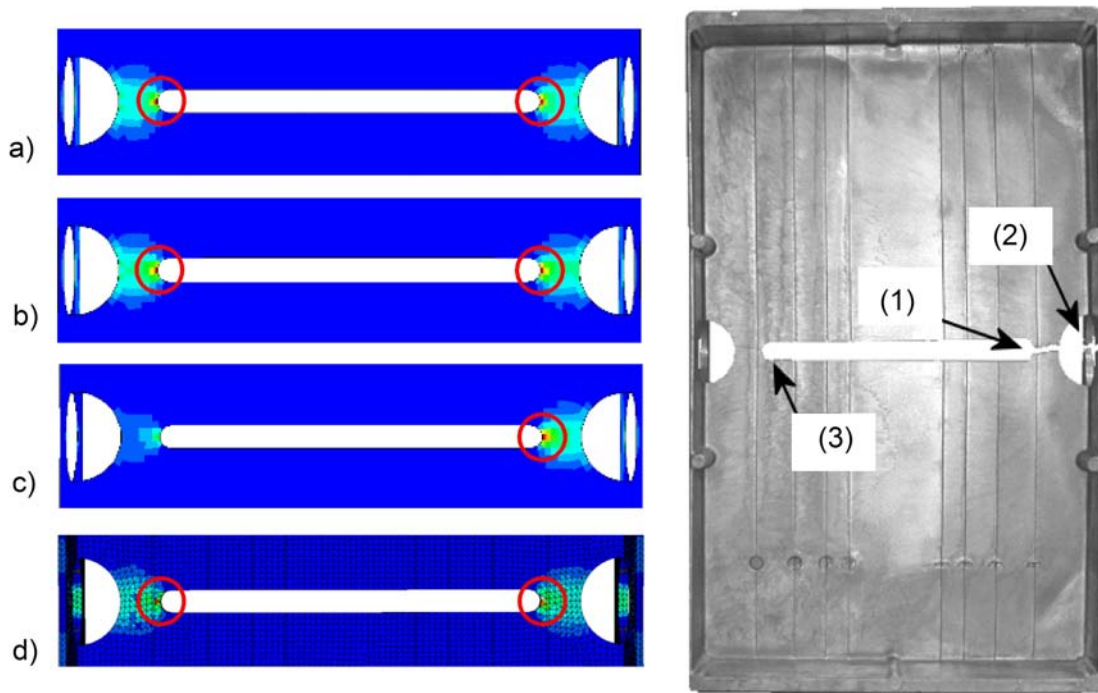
Vergleich der Anrissorte aus Simulation und Bauteilversuch (Anguss rechts)
